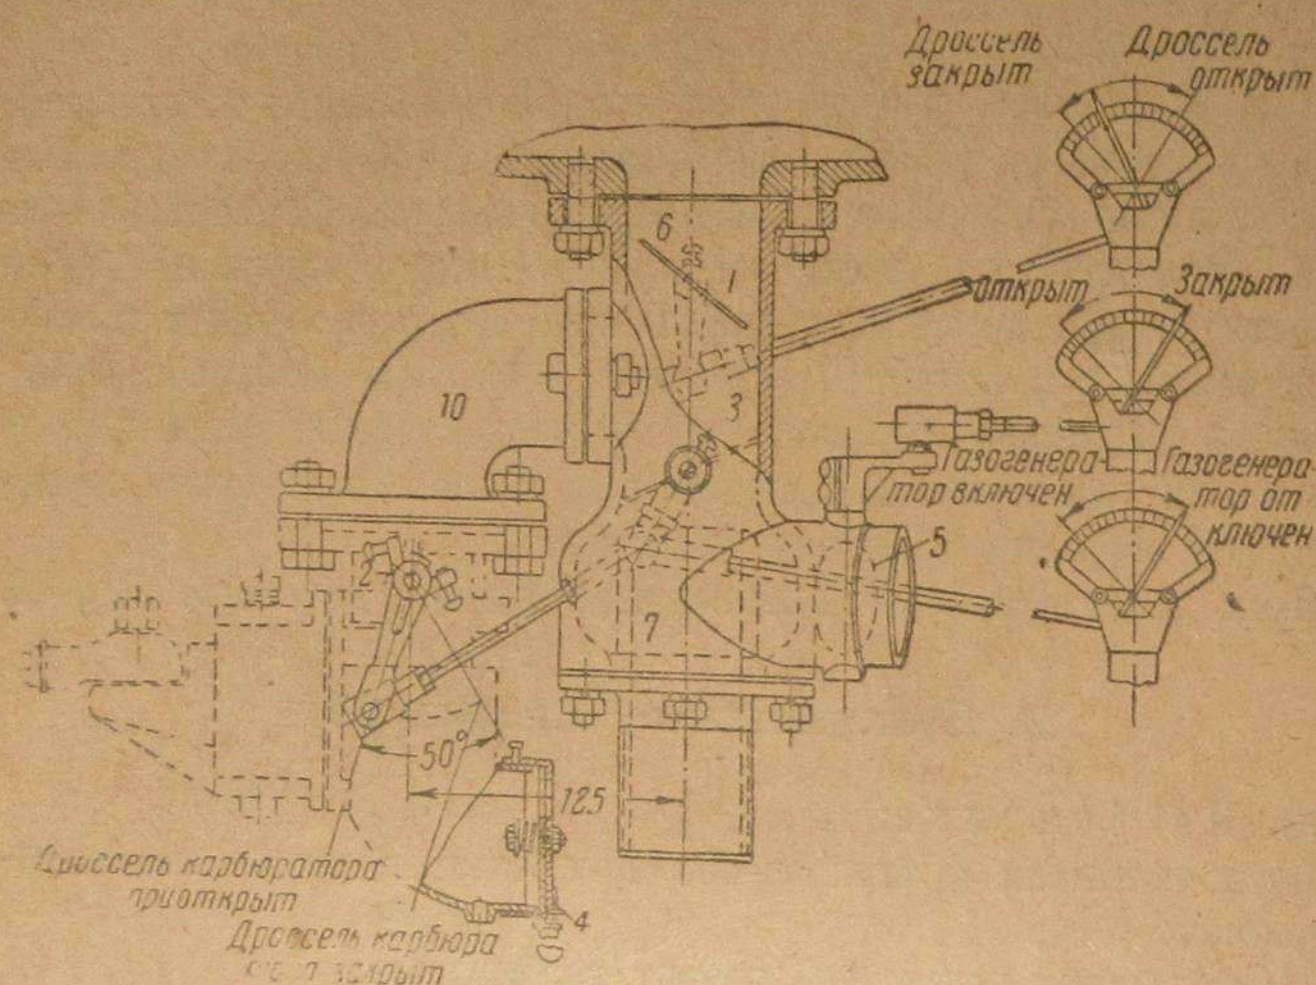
Смеситель газа двигателя ЧТЗ «Сталинец-60»: 1 — корпус смесителя, 2 — ось дросселя карбюратора, 3 — заслонка газовоздушной смеси, 4 — заслонка карбюратора, 5 — заслонка воздуха, 6 — дроссельная заслонка, 7 — газовый патрубок, 10 — бензовоздушный патрубок
